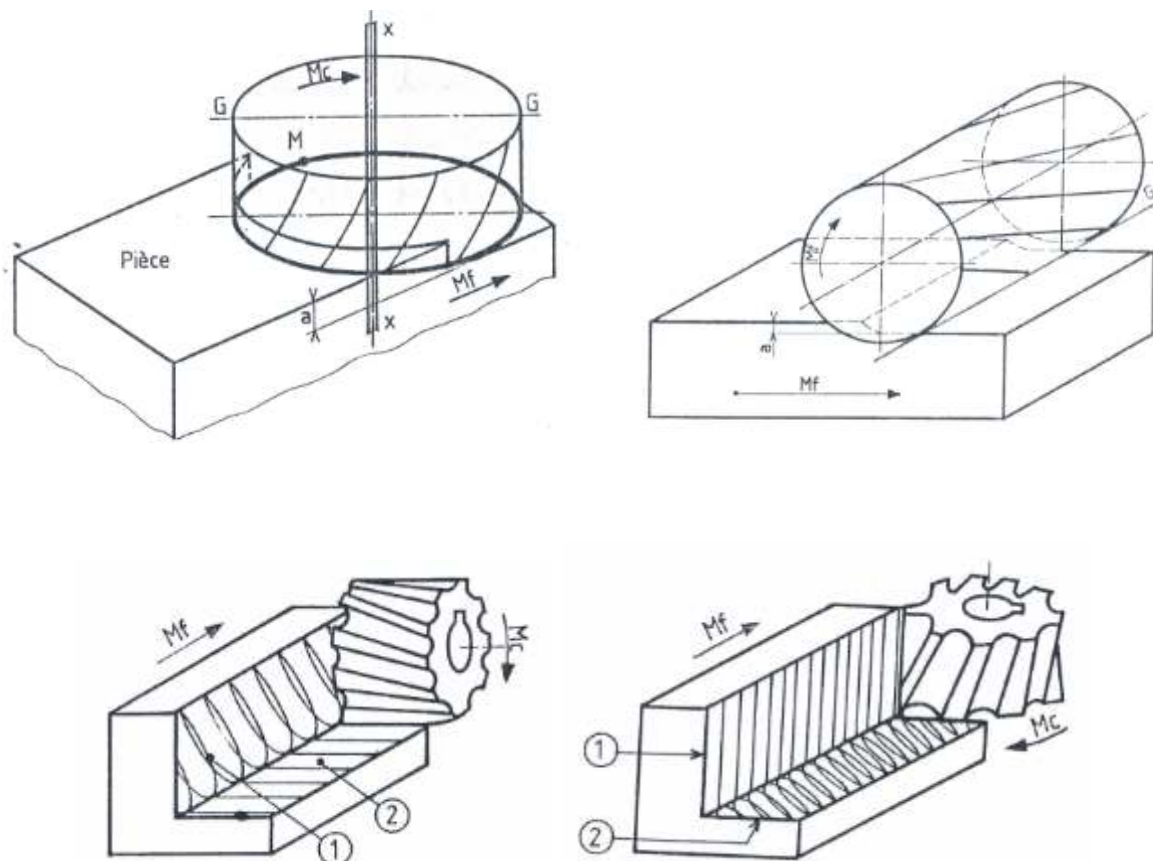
Mode de génération des surfaces par fraisage :
